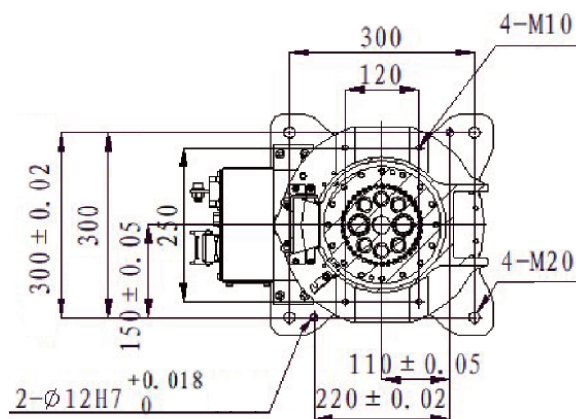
Габаритные чертежи робота-манипулятора SP180-3200.
